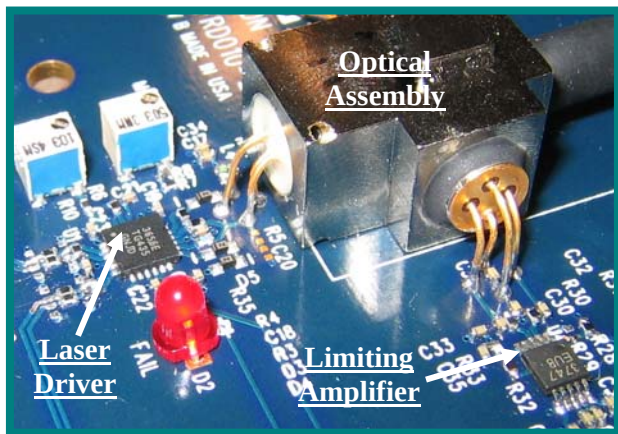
PCB 顶装激光器组件 (图中所示为 HFRD 10.2)
